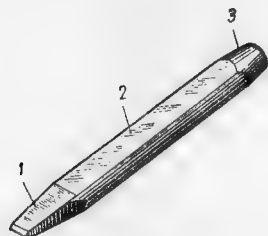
1—рабочая часть; 2—корпус; 3—ударная часть
